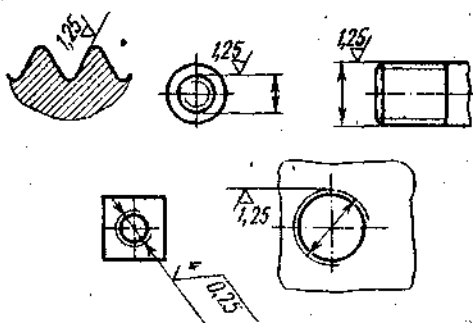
Нанесение обозначений шероховатости поверхностей резьбы
